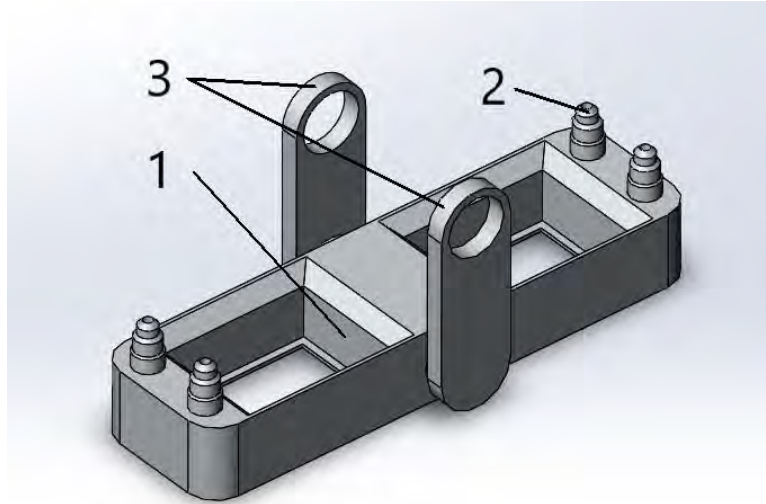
Зовнішній вигляд корпусу блоку первинних перетворювачів
